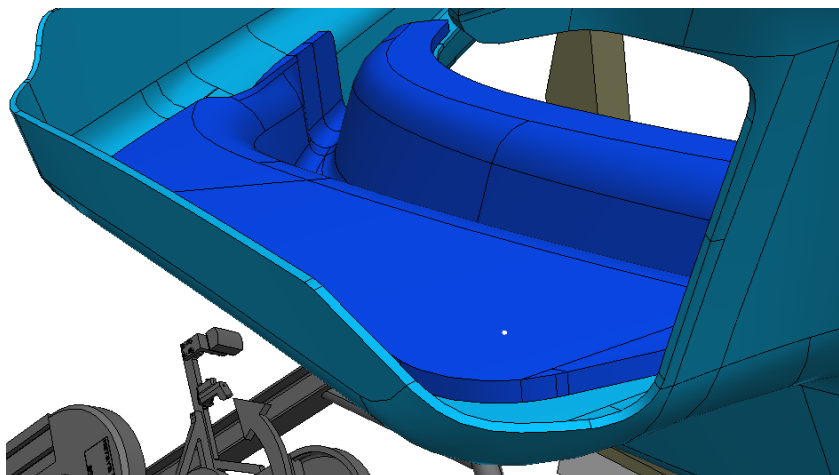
Соединение деталей сварочной точкой
